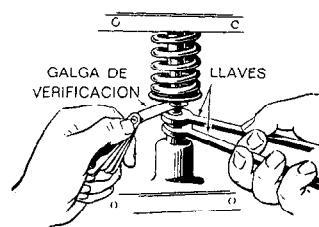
Ajuste del reglaje de taqués en un motor con válvulas laterales.
